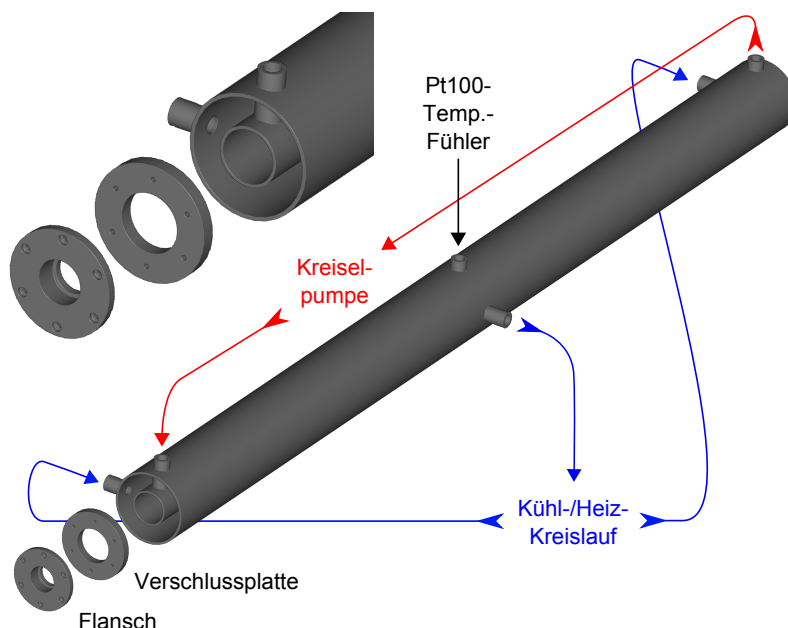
CAD-Zeichnung der verwendeten Wasserrohre. Alle dargestellten Teile bestehen aus rostfreiem Edelstahl. Innen- und Außenrohr sind über die Verschlussplatte miteinander verschweißt. Im aufgeschraubten Flansch ist das optische Zugangsfenster eingeklebt. Das Innen- bzw. Außenvolumen ist über die drei oberen bzw. seitlichen Stutzen zugänglich. Die Pfeile repräsentieren Kunststoffschläuche und weisen in Fließrichtung der Wasserkreisläufe. Im Außenvolumen zirkuliert Heiz- oder Kühlwasser zur Temperierung des Probenwassers im Innenvolumen. Die Umwälzung des Probenwassers reduziert dessen Temperaturunterschiede auf unter $0,1^{\circ}\text{C}$. Über den mittleren Stutzen ist ein Temperaturfühler knapp oberhalb des auf der optischen Achse traversierenden Laserstrahls positioniert.
